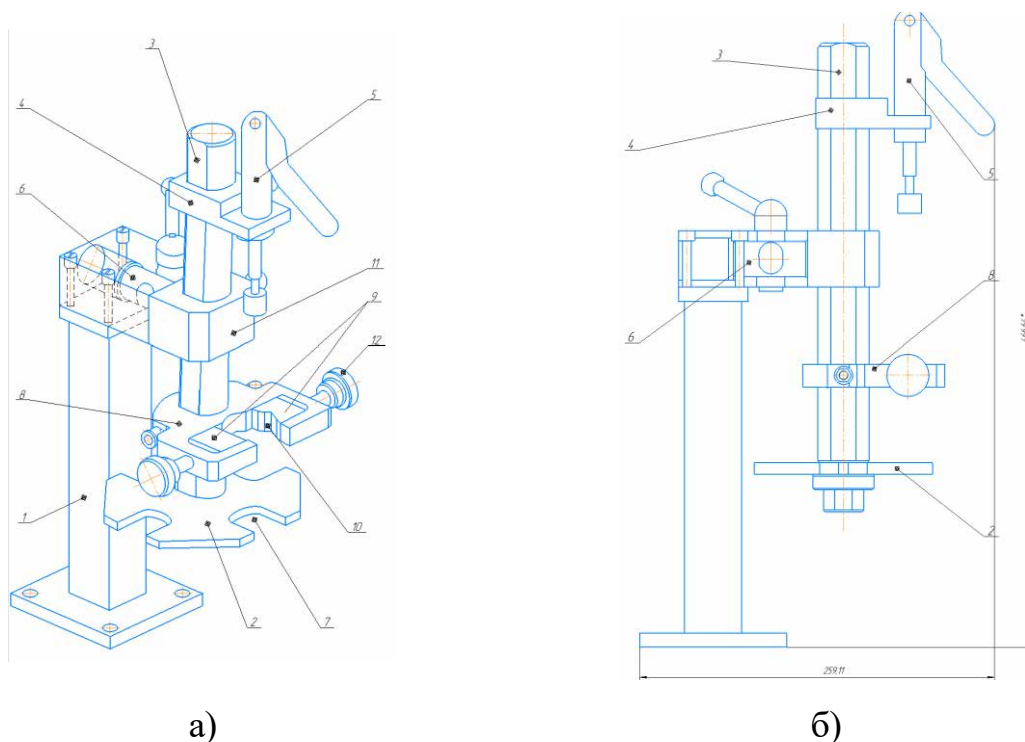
Загальний вигляд прототипу пристрою (а) та схема пристрою на вигляді збоку (б): 1 – опорна стійка; 2 – фіксуєюча пластина; 3 – напрямна штанга; 4 – каретка; 5 – осьовий затискач; 6 – рухома вісь; 7 – паз для фіксації корпусу форсунки; 8 – бічний фіксатор; 9 – затискні губки; 10 – клиновидна виїмка; 11 – корпус; 12 – затискний гвинт
